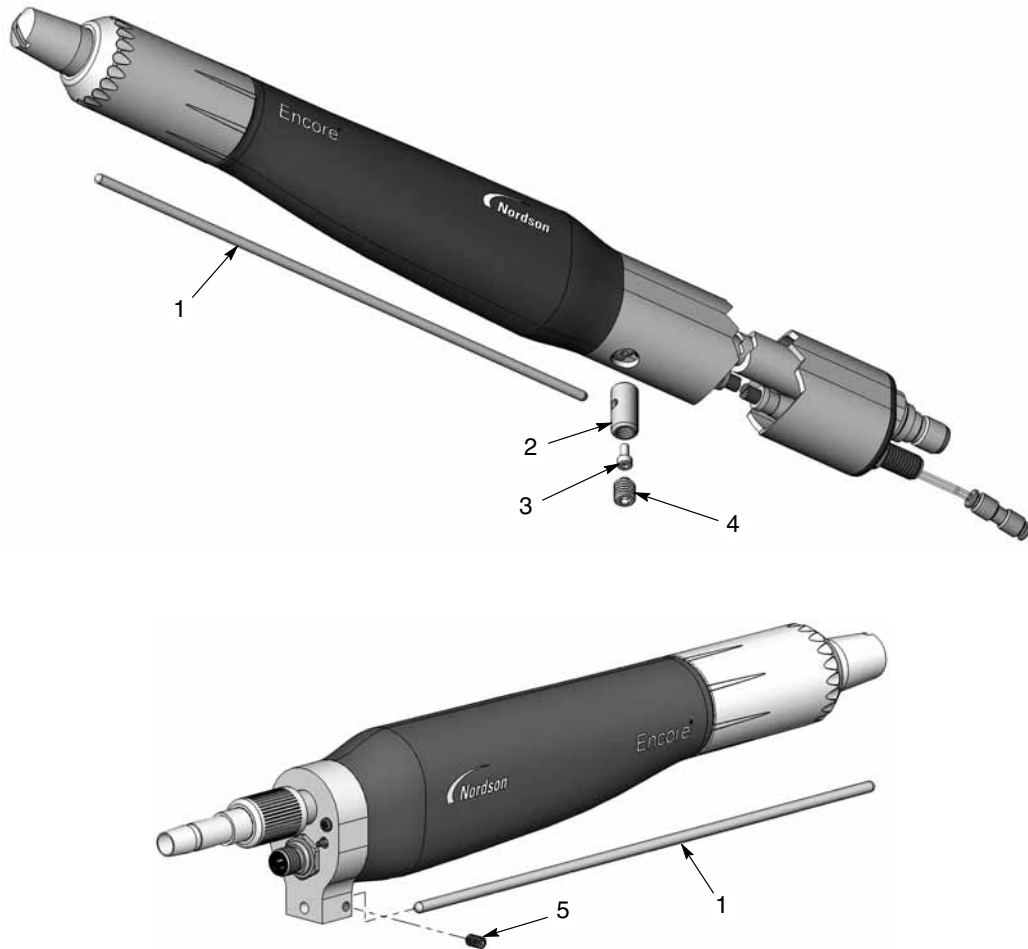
Pistoolstang voor stangbevestigde pistolen
